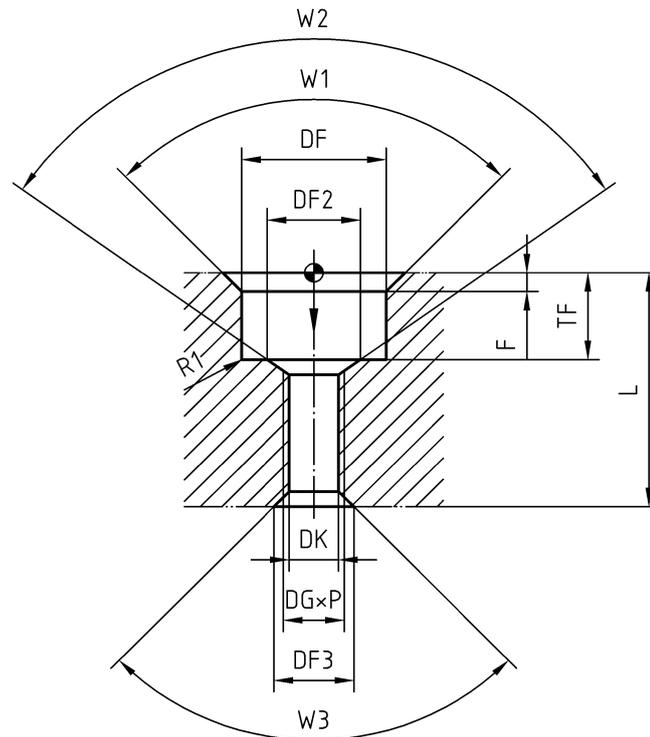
Gewindedurchgangsbohrung mit Flachsenkung
